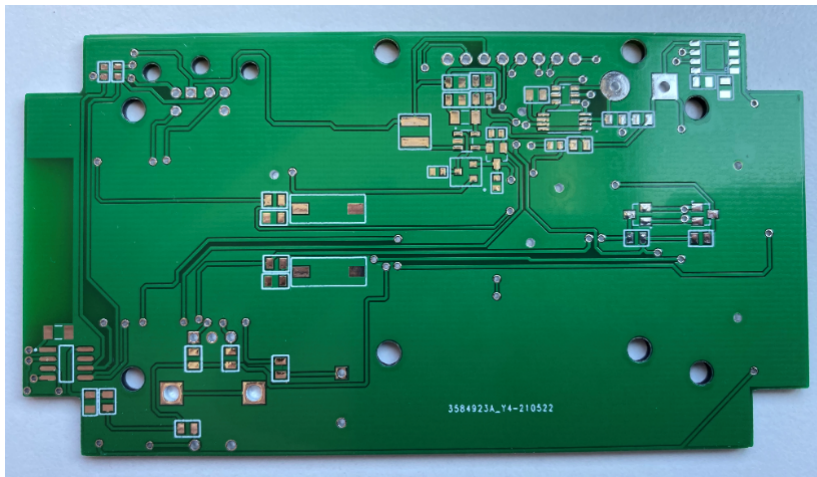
Vista inferior PCB fabricada por JLCPCB
